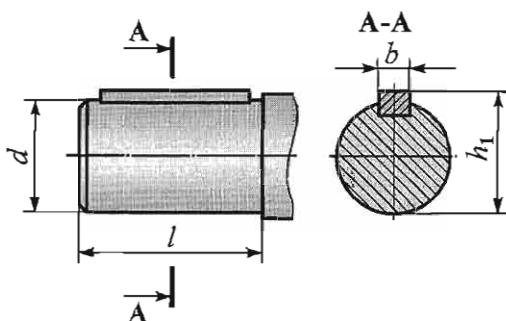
Размеры конца тихоходного вала мотор-редуктора
